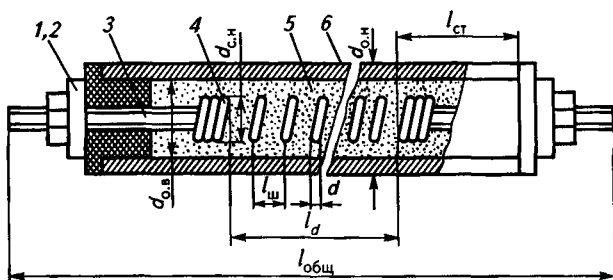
Трубчатый электронагреватель (ТЭН):
